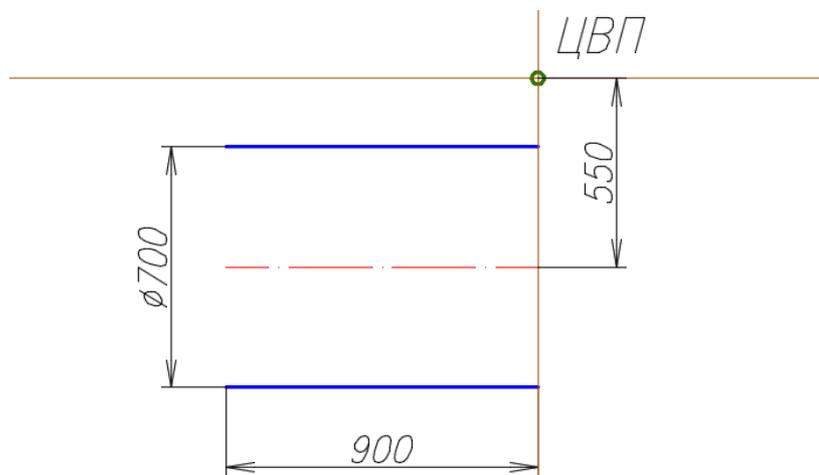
Чертеж левой части трубы для подачи загрязненного воздуха
